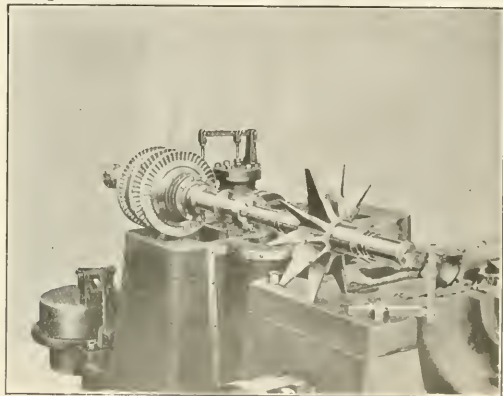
ÁRBOL ROTOR DE LA TURBOPRESORA
